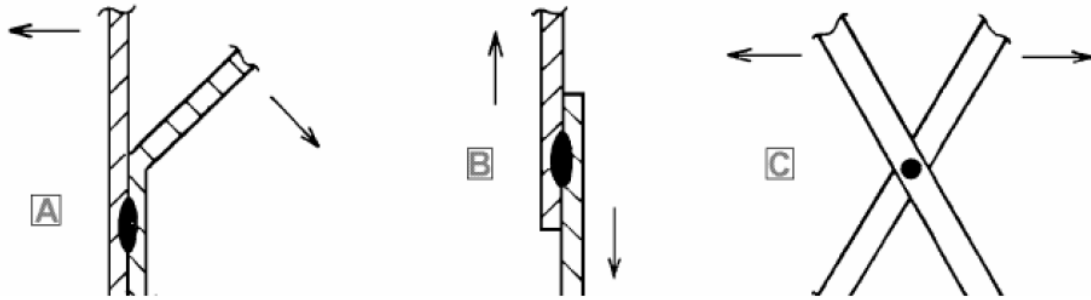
Ensaio por arrancamento (A) Tração (B) e Torção (C) - Fonte: WELDING SCIENCE, 2009
